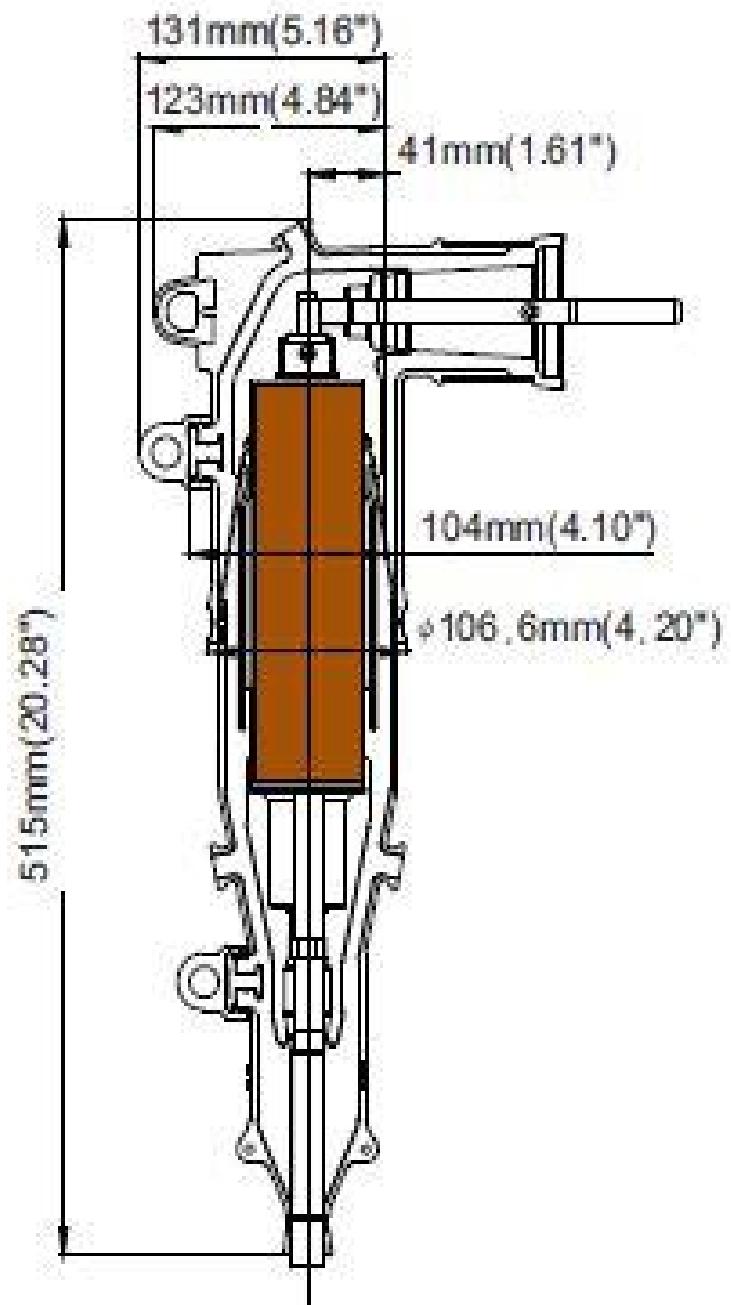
Dimensiones de codo con fusible Hi-Tech™ Instalado.
